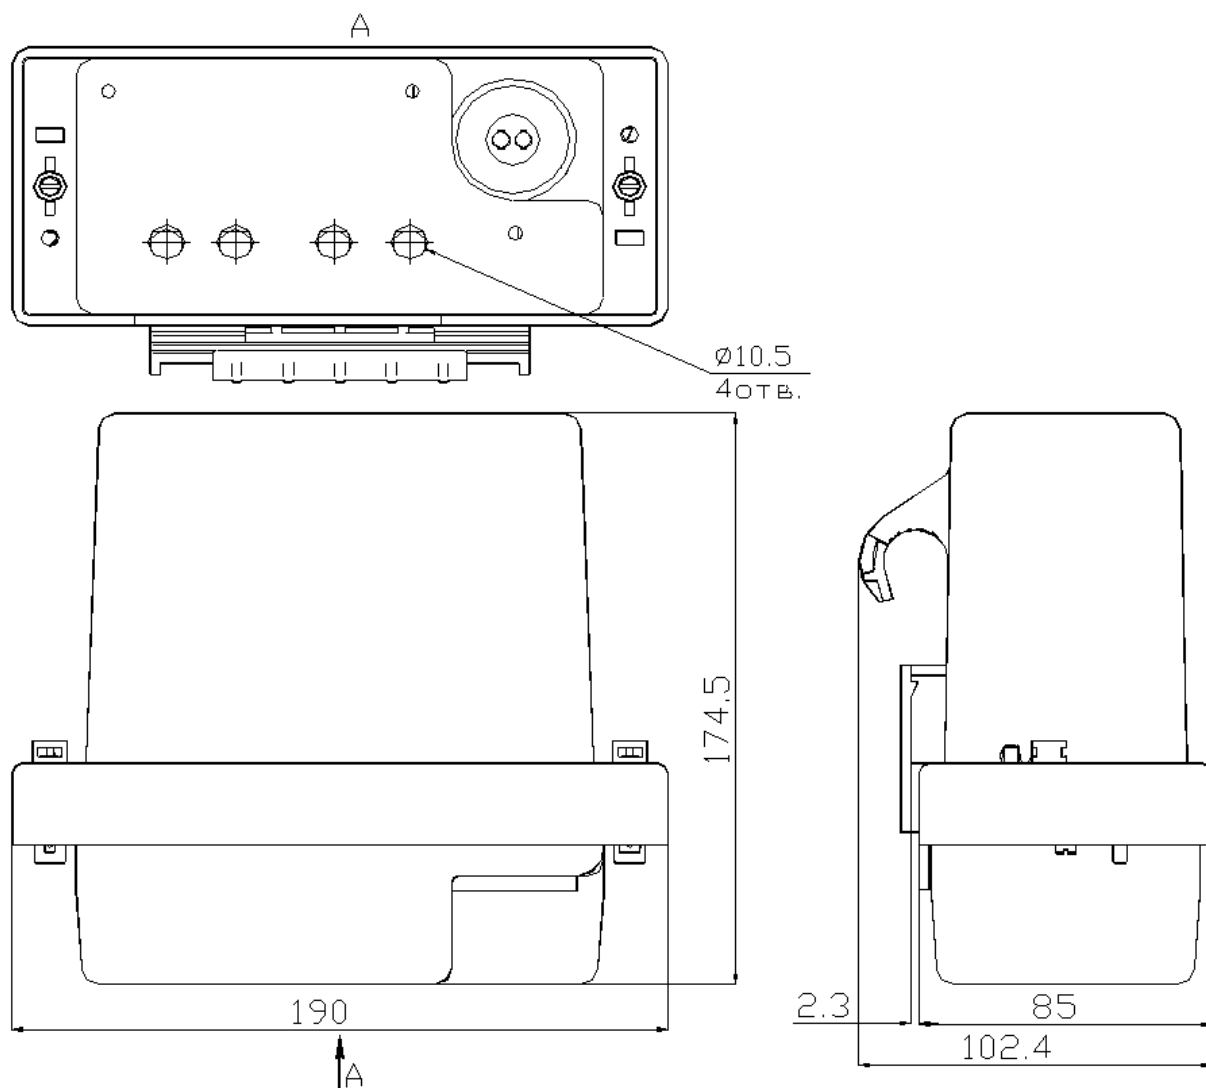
Габаритные и установочные размеры устройства M22.003.00.000-02
